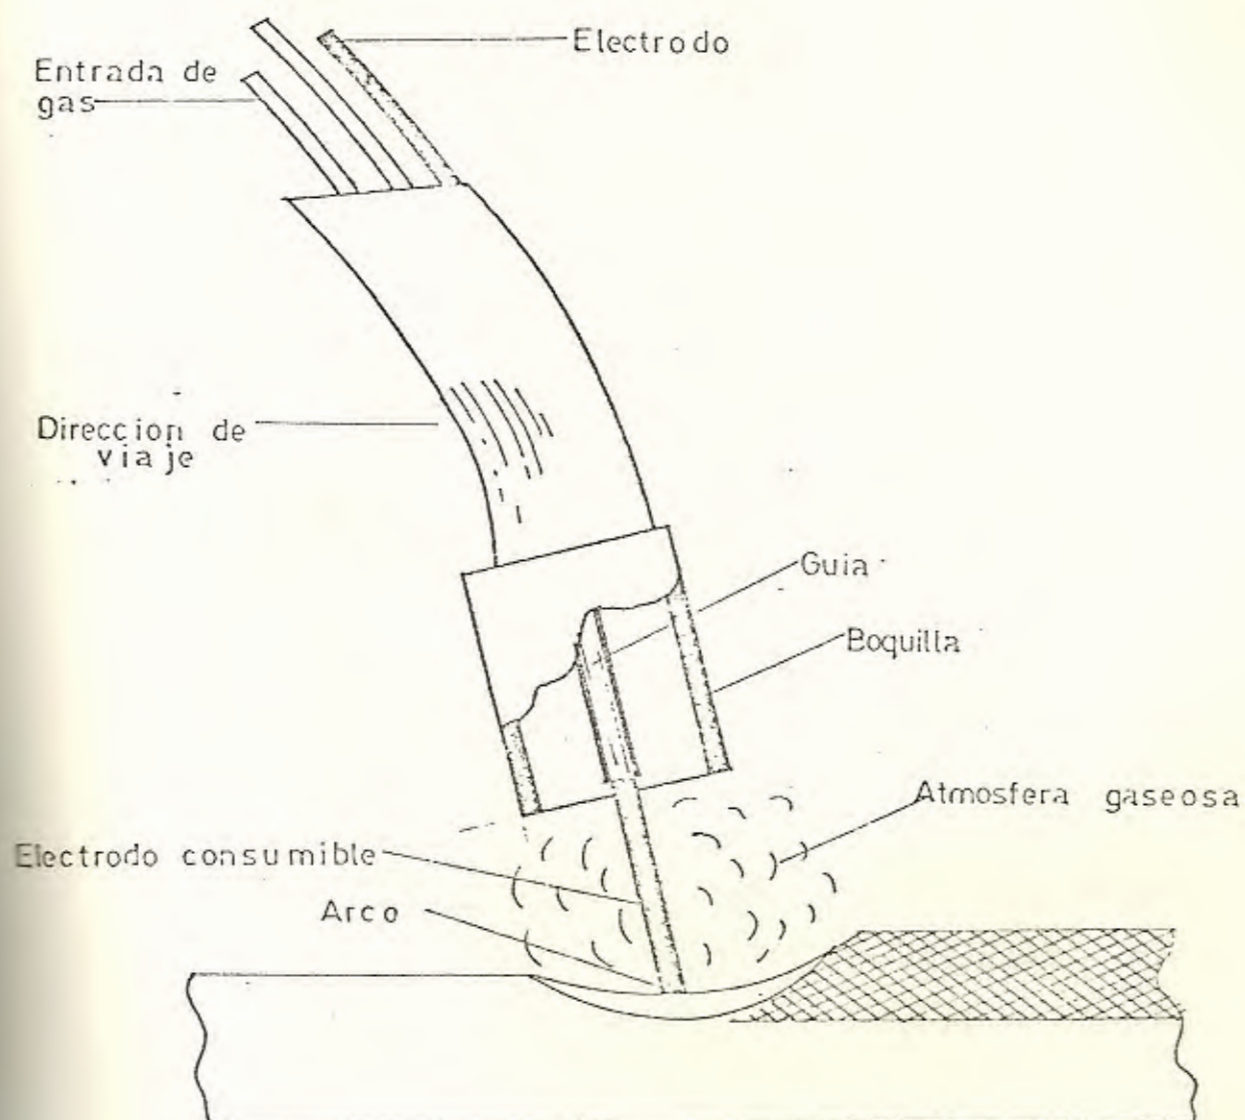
SOLDADURA AL ARCO EN UN PROCESO MIG
